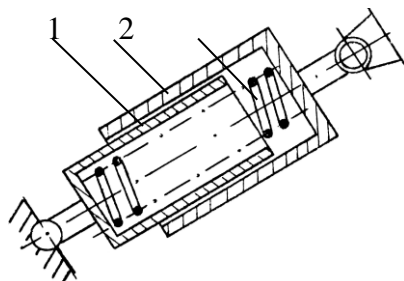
Пружинний зрівноважувальний механізм:
